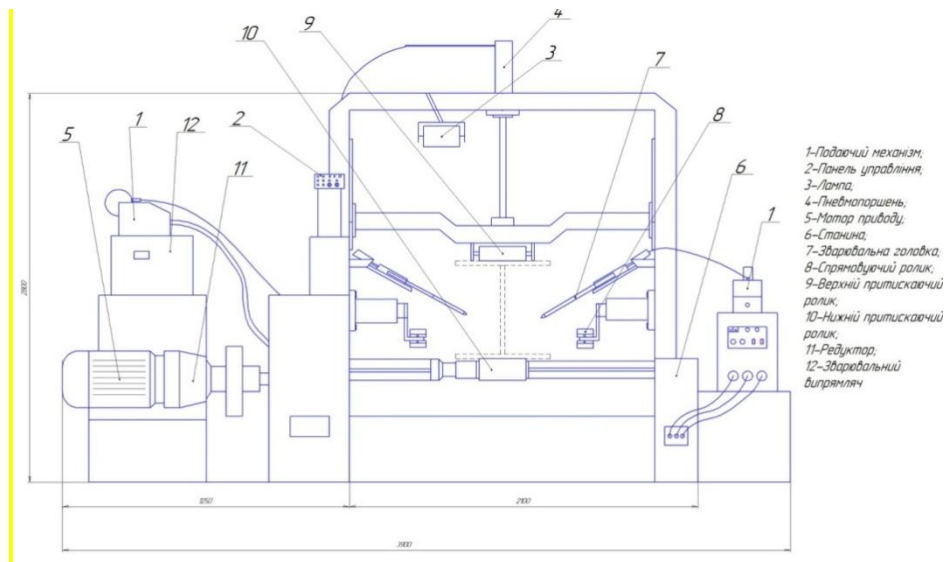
Загальний вигляд порталної установки для зварювання
